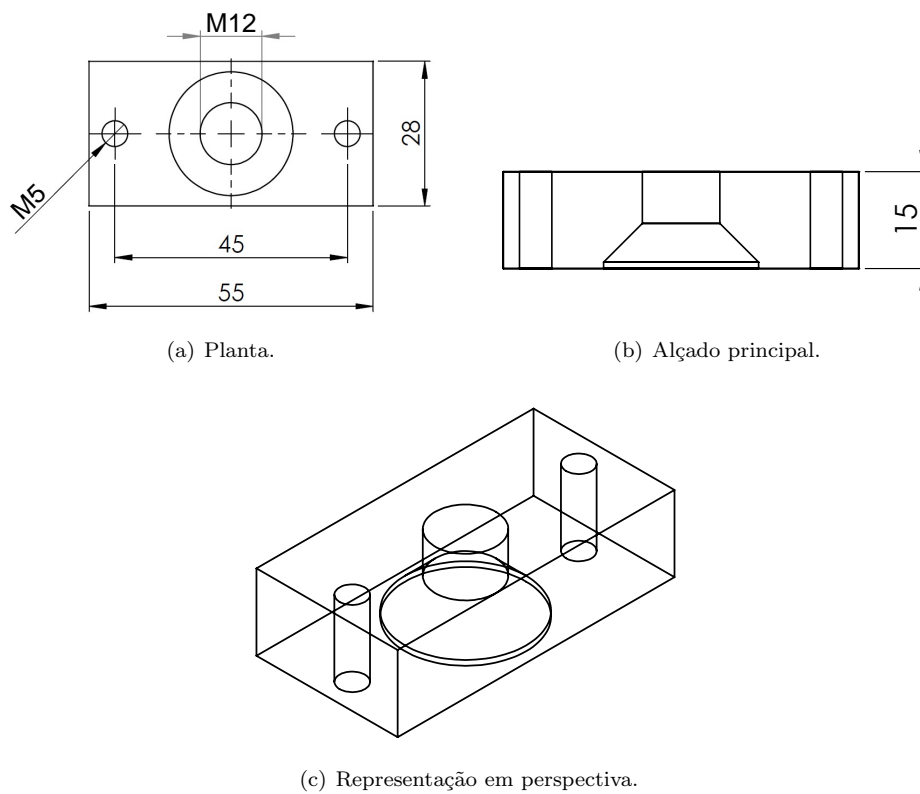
Desenho técnico da placa de interface (dimensões em mm).
